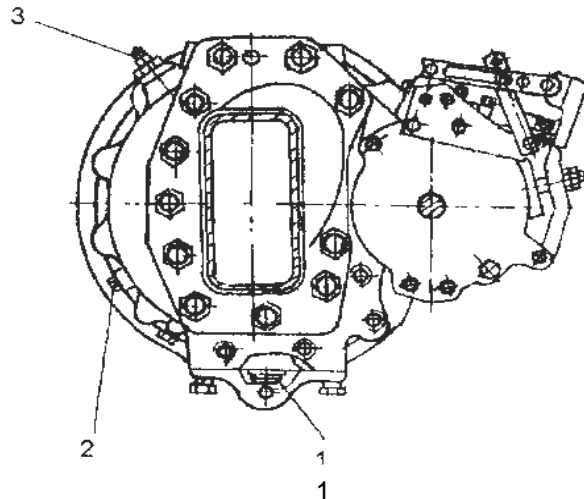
Бортовой редуктор (вид со стороны тормоза): 1 – пробка отверстия для слива масла из редуктора; 2 – пробка контрольного отверстия уровня масла; 3 – пробка заливного отверстия
